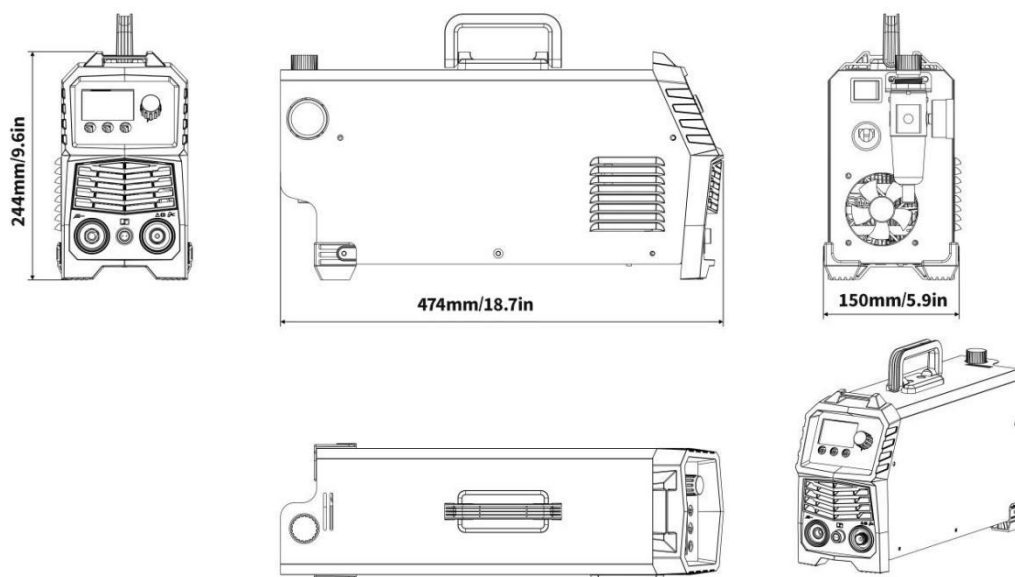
Apparence et taille de la machine (Unité : mm / pouce)
